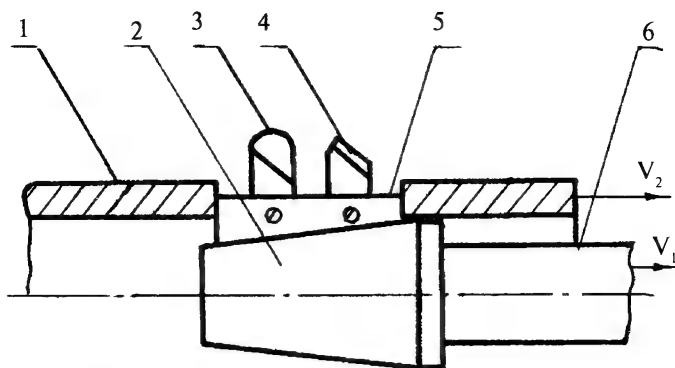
Клиновое приспособление: 1 - корпус, 2 - клин, 3 - чистовой резец, 4 - черновой резец, 5 - колодка, 6 - тяга
